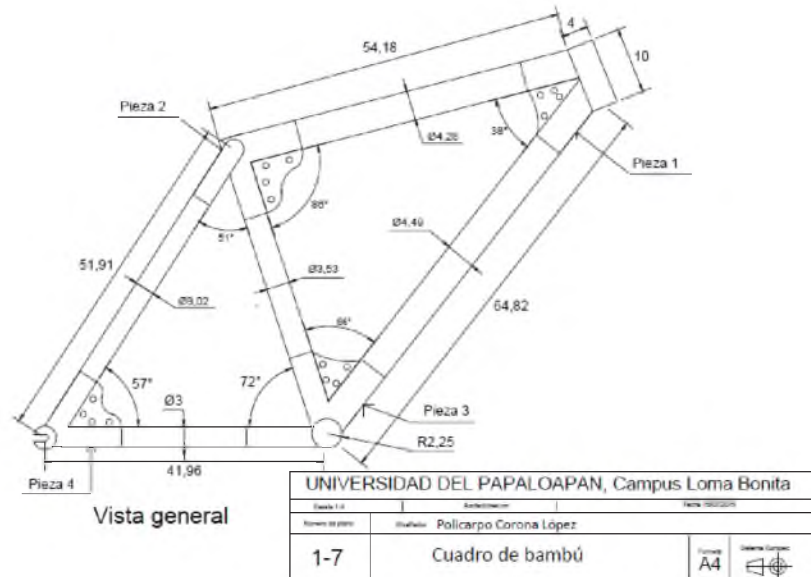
plano del cuadro con las medidas reales para su fabricación.
